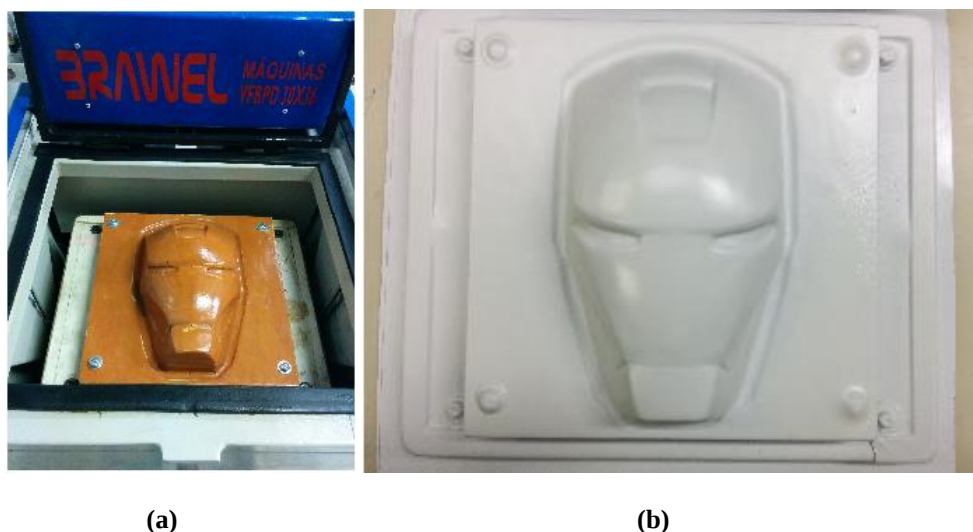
(a) Fixação do molde no equipamento de termoformagem; (b) resultado da operação – produto final
